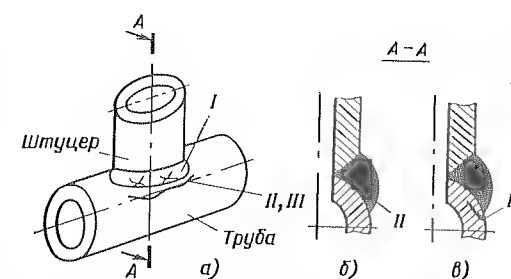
Схема расположения трещин в сварных тройниках:
